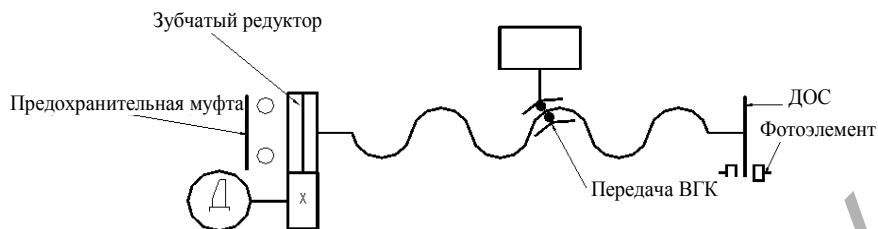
Тяговый механизм подачи с зубчатым редуктором на ходовом винте
